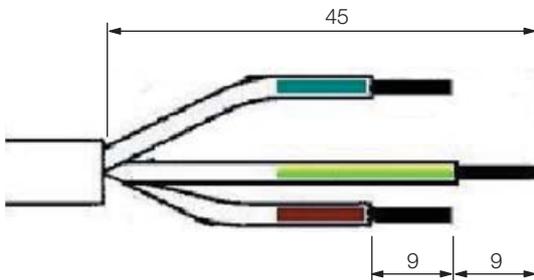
Maße zum Entfernen der Gummiummantelung und der Isolierung
